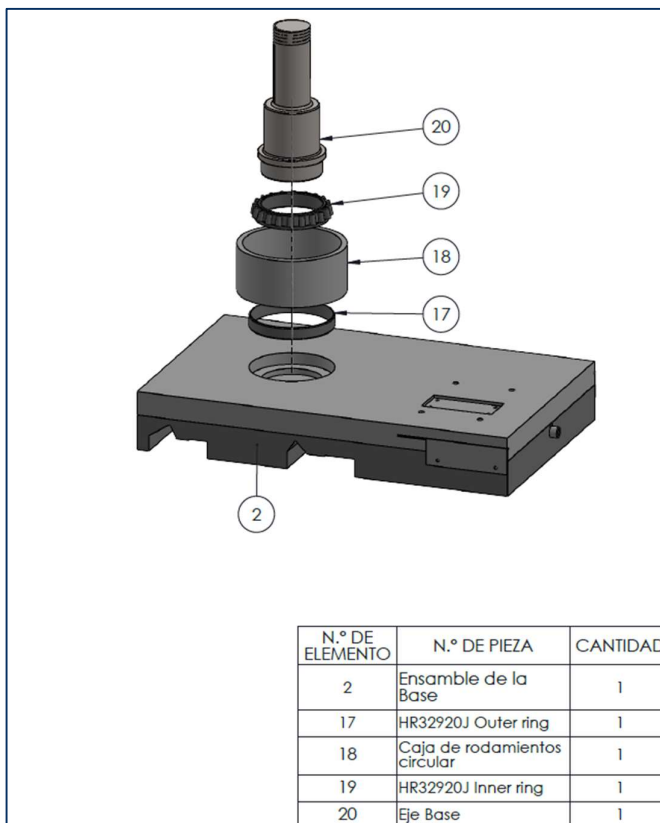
ensamble base adaptable a torno con caja de rodamientos, rodamientos cónicos simple y doble, eje.
